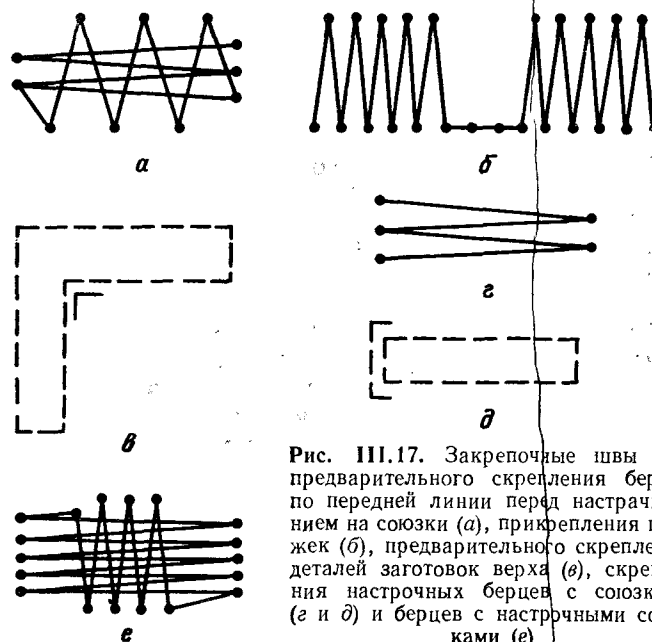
Закрепочные швы для предварительного скрепления берцов по передней линии перед настрачиванием на союзки (а), прикрепления пряжек (б), предварительного скрепления деталей заготовок верха (в), скрепления настрочных берцов с союзками (г и д) и берцов с настрочными союзками (е)
